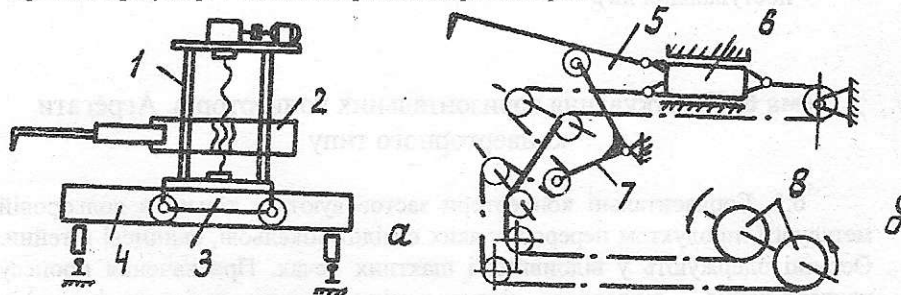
Схеми машин для згортання шлаку з міксеру (а) і ковша (б): 1-направляючі; 2-вертикально рухома каретка; 3-візок; 4-міст; 5-штанга; 6-каретка; 7-двоплечий хитний важіль; 8-лебідка
